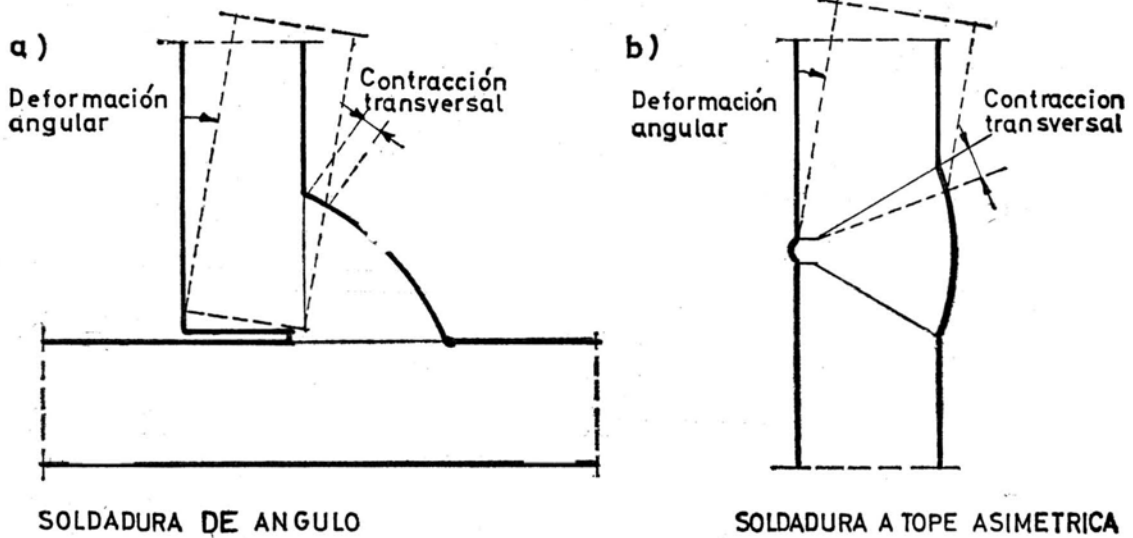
DEFORMACIONES ANGULARES POR LA SOLDADURA
